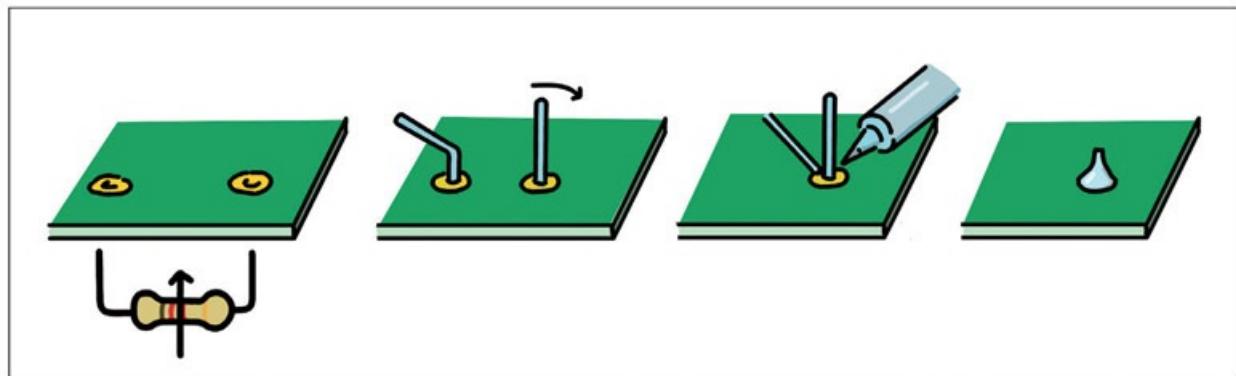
Soldadura de un componente sobre un circuito impreso.
